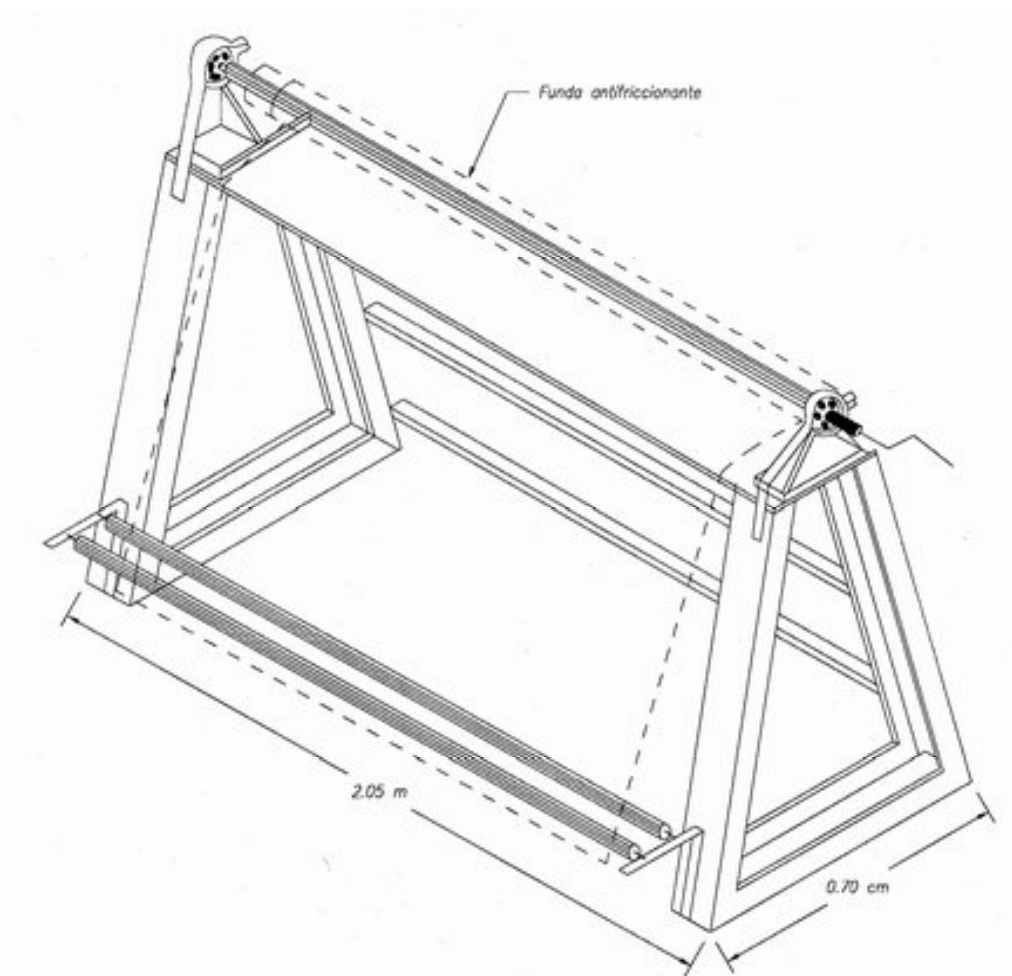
, Rodillo posicionado de membrana antifriccionante
